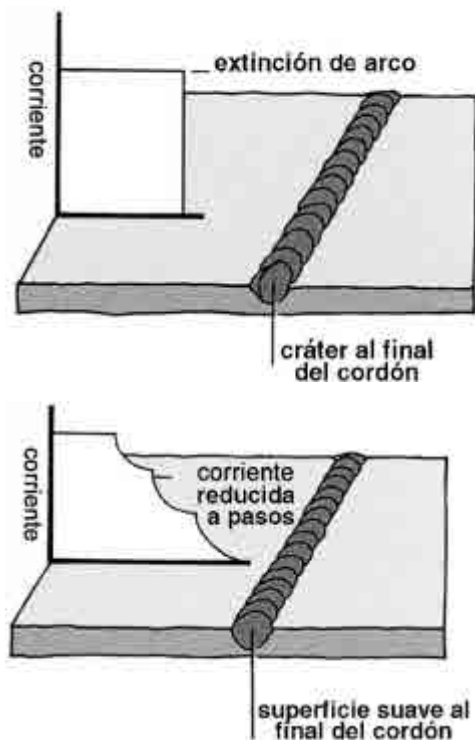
Intensidad del cordón soldadura TIG.
